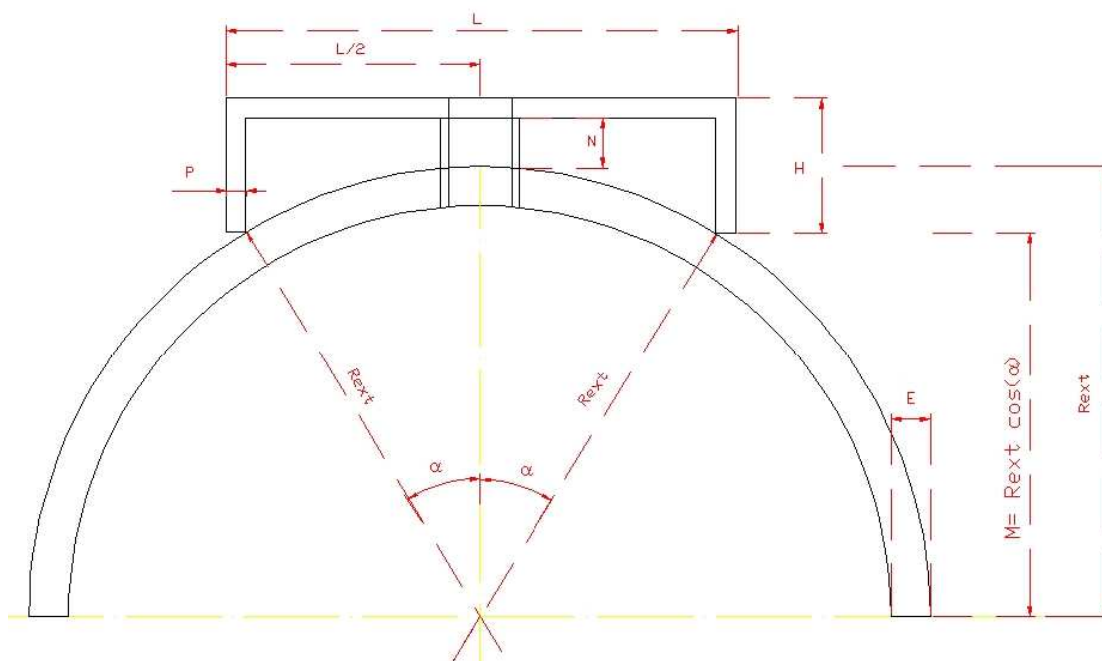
Esquema geométrico bidimensional do suporte sobre a secção de medição.
